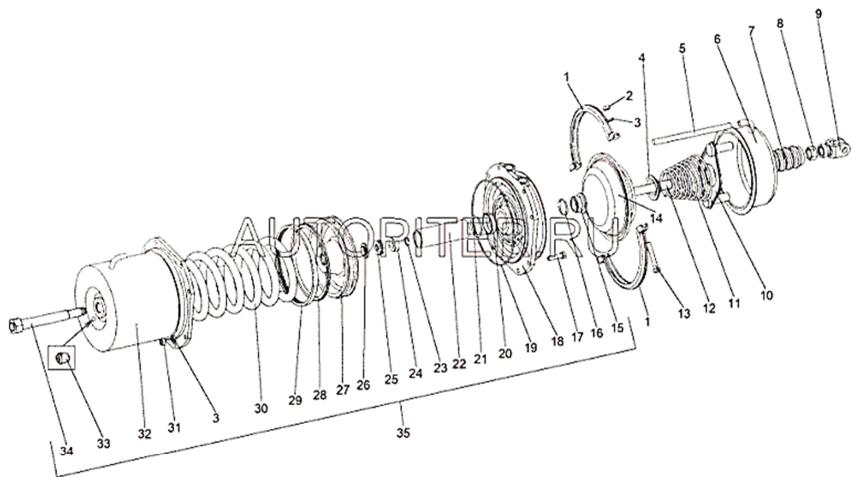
Тормозная камера типа 20 (рассматриваемая в курсовом проекте деталь № 18 – корпус 6923-3519242)
